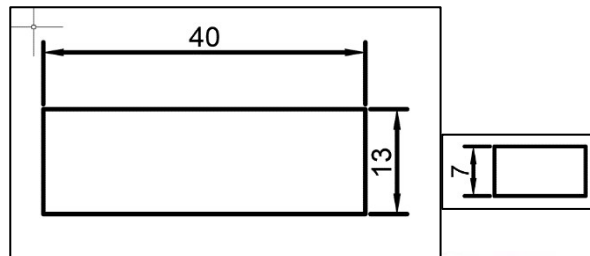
Dimensi Spesimen Uji Tarik ASTM D638 [25]
